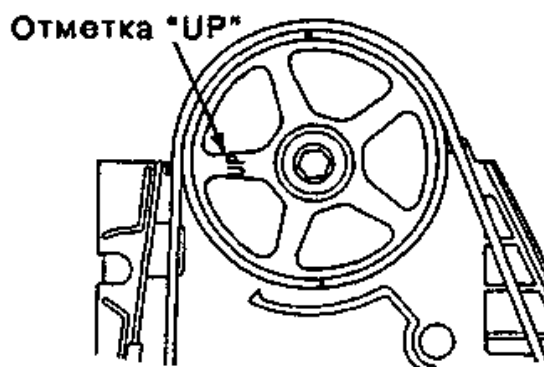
Положение шкива распределителя при регулировке натяжения ремня
